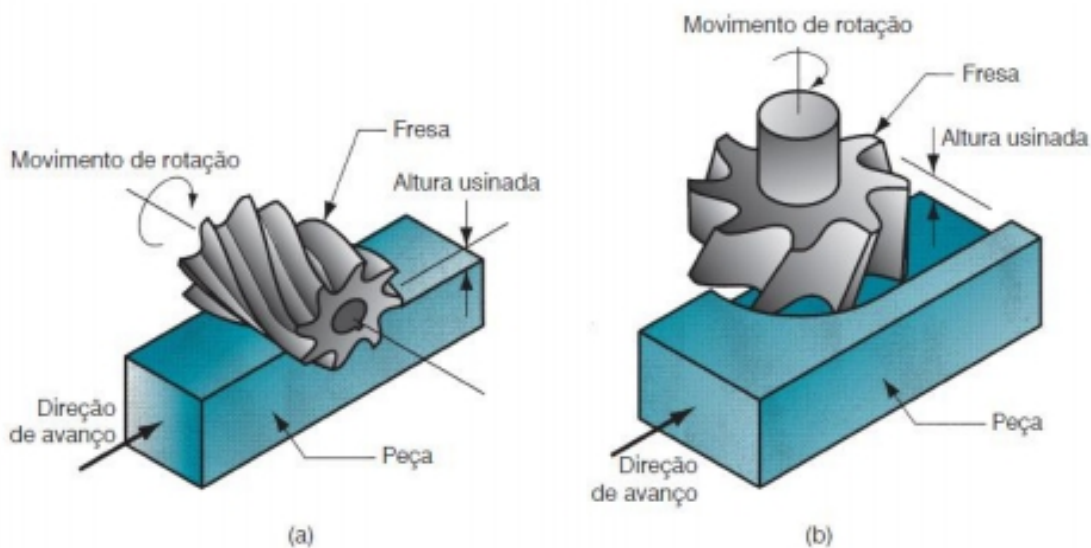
Tipos de máquina-ferramenta, (a) fresadora horizontal e (b) fresadora vertical.
